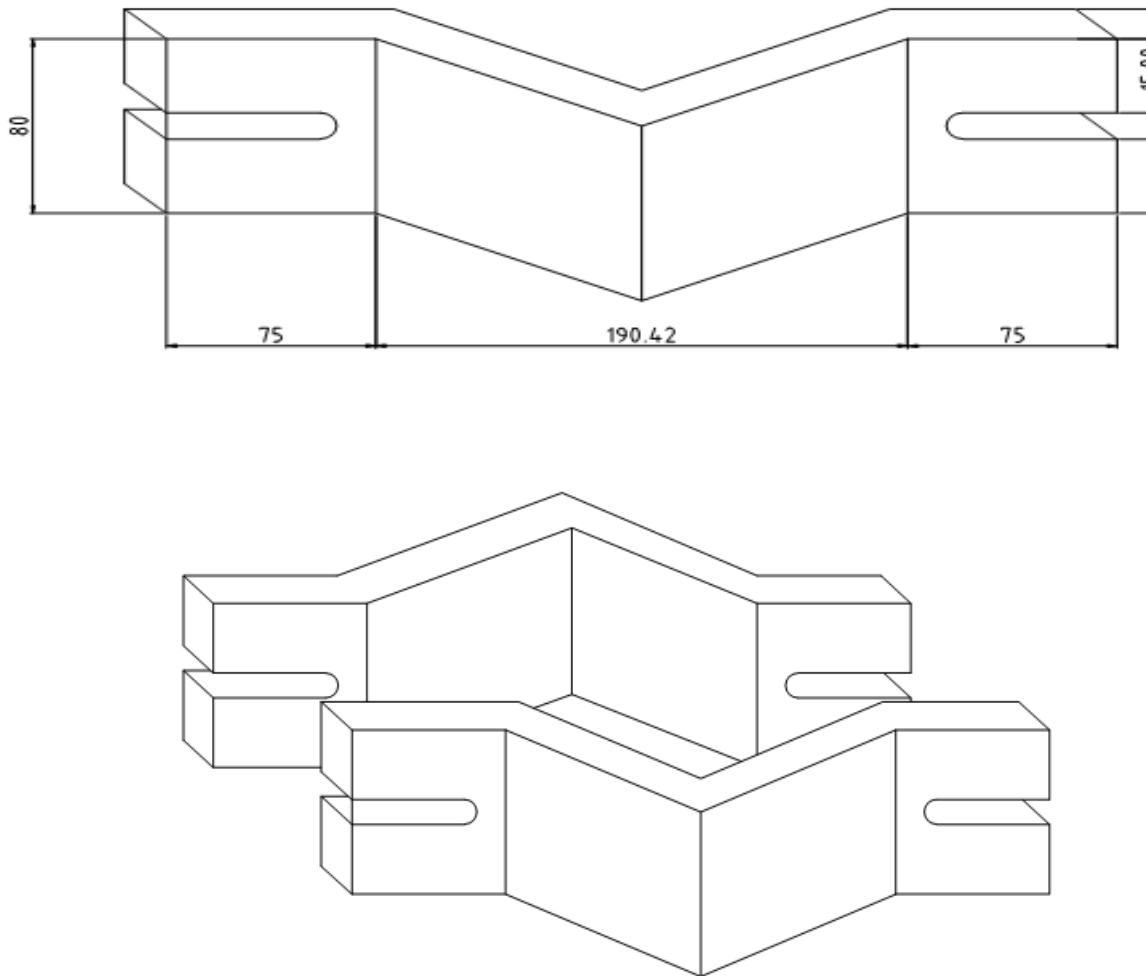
Staffe di serraggio (dimensioni in mm e 3D)
